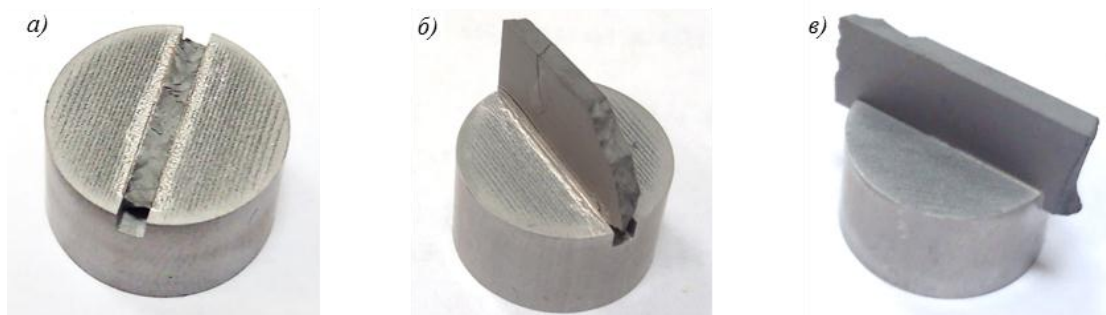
Внешний вид образцов из сплава ЭП648 с ККМ после пайки с различными способами питания припоем:
